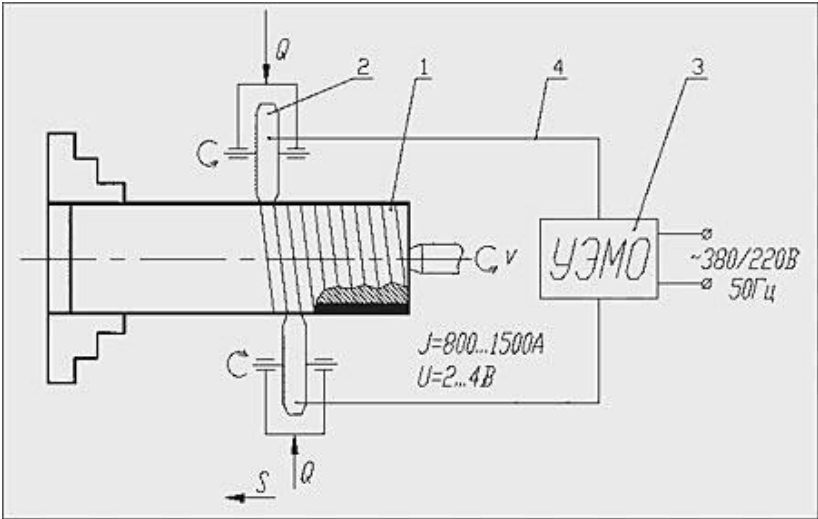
Схема электромеханической закалилки на токарно-винторезном станке
